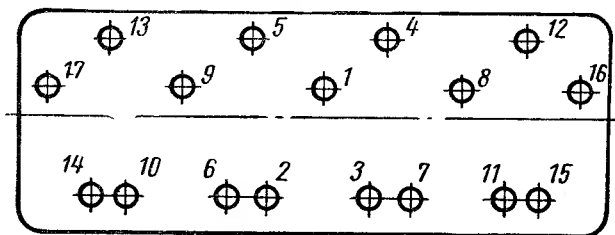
Схема последовательности затяжки болтов, крепящих головки цилиндров двигателя ЗИЛ-130
